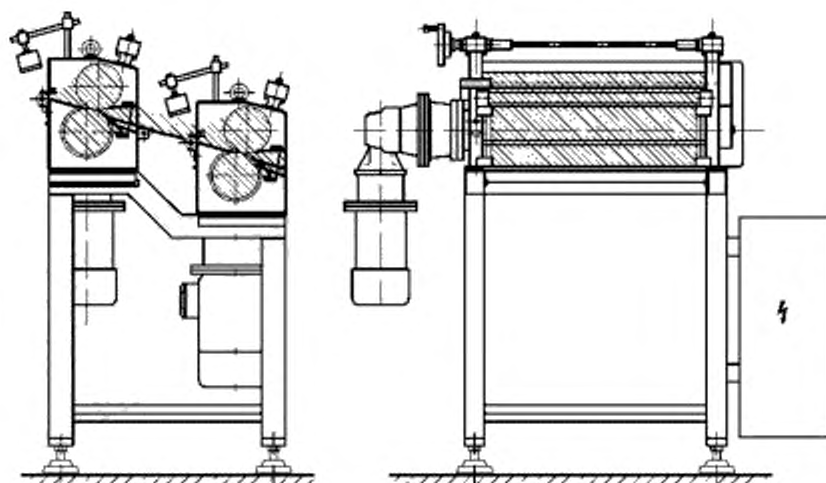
Вальцовая машина для калибровки заготовок из теста
